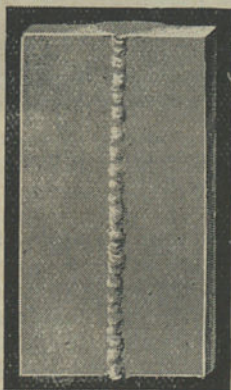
Avêso duma soldadura perfeita e regularmente atravessada.
